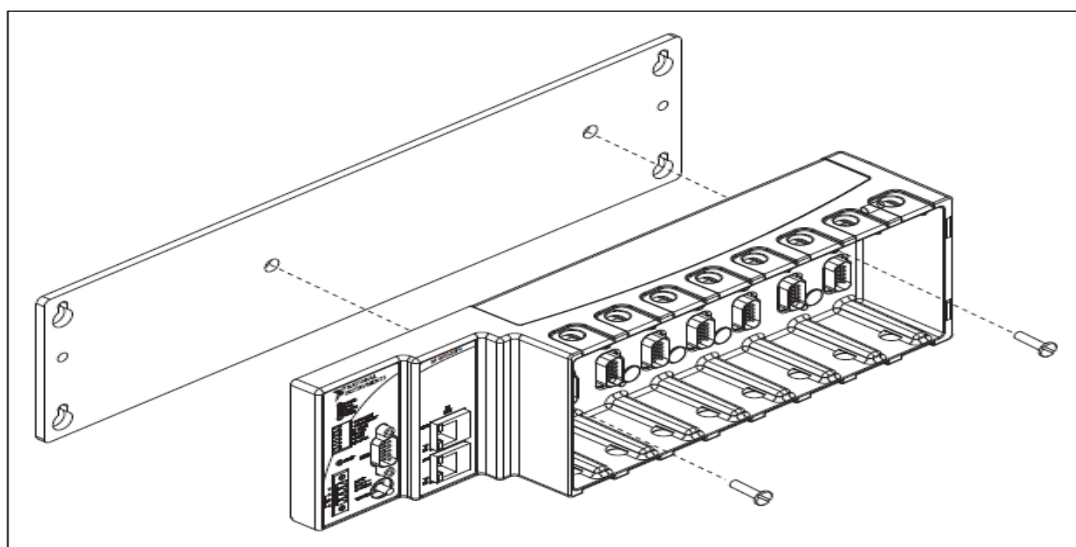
Instalación y Montaje de Accesorios en el Panel del cRIO-9074
